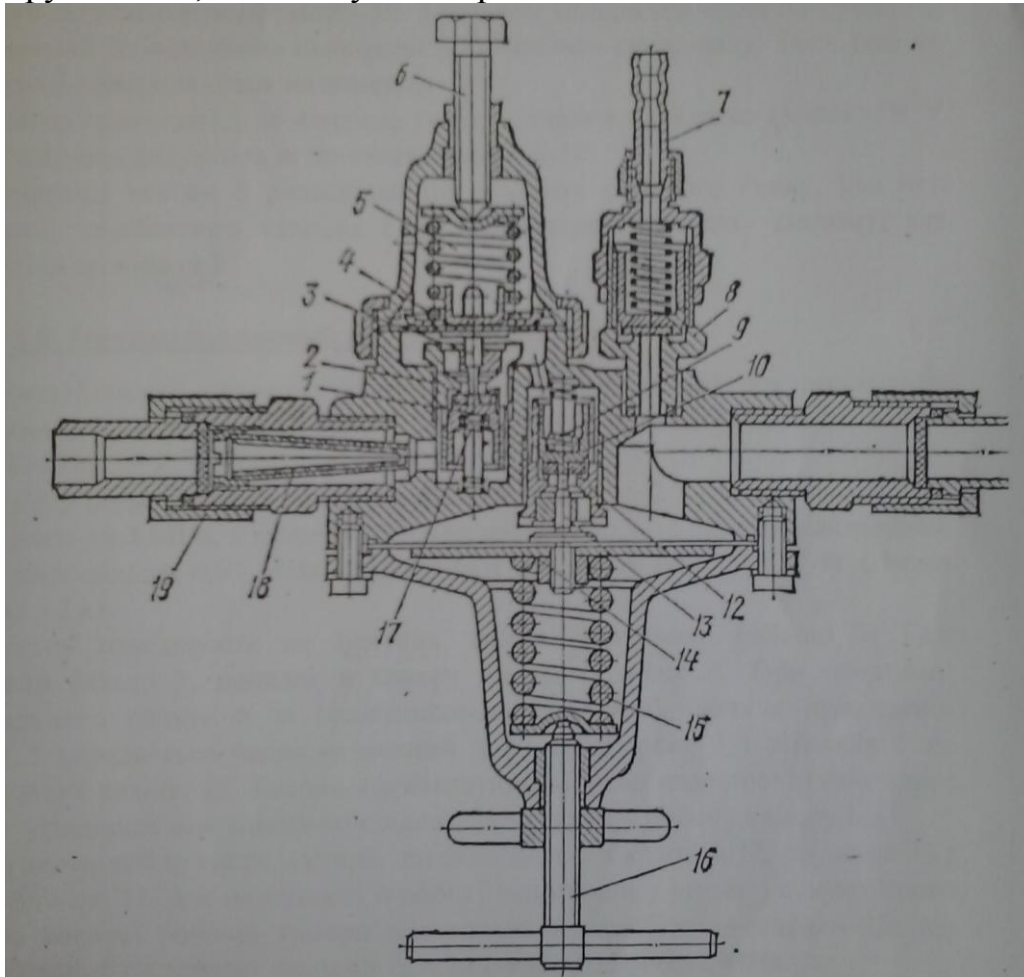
Схема ацетиленового редуктора РАД – 30-1
